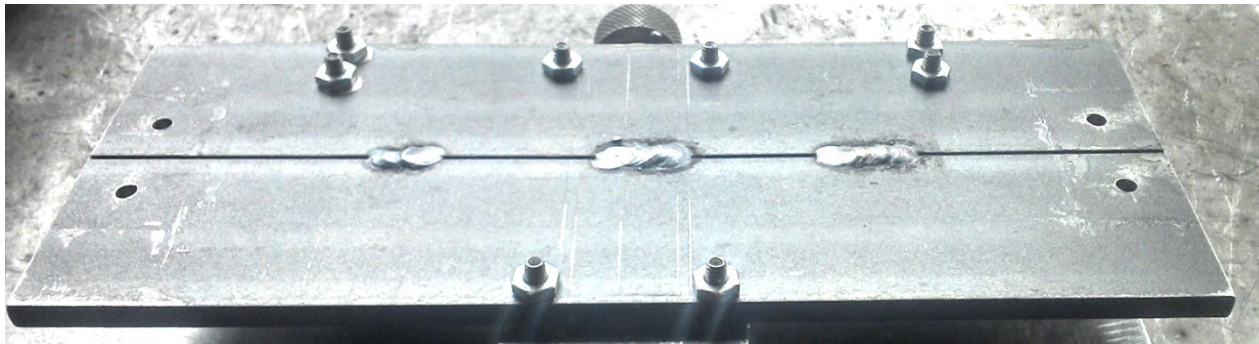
Placa base del mecanismo. Esta pieza es la base del mecanismo y en ella se ensamblan piezas del sistema de avance seleccionado.
